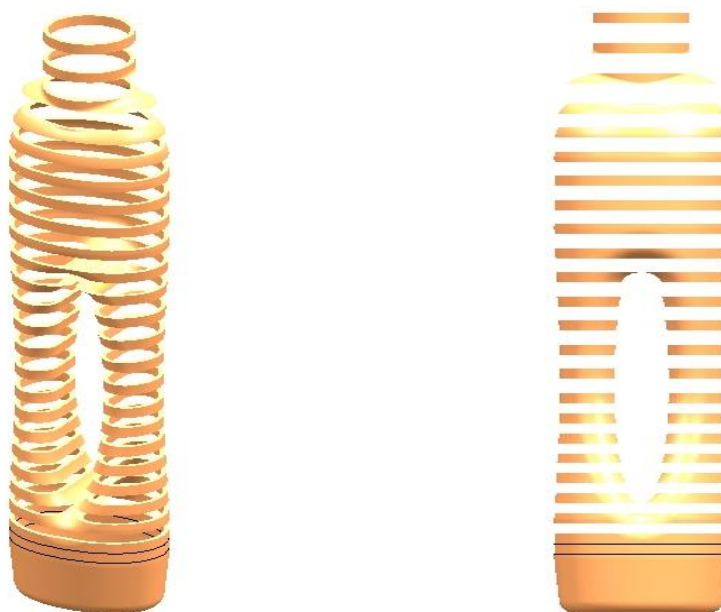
Construção do modelo por montagem das sucessivas camadas seccionadas.
